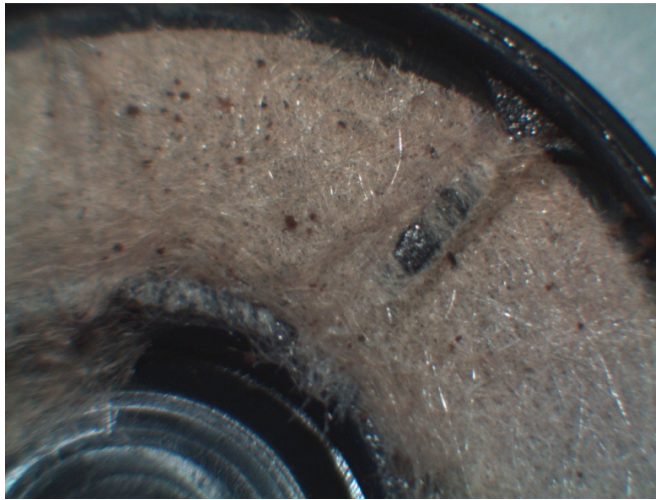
Pormenor da soldadura do filtro após a lavagem
